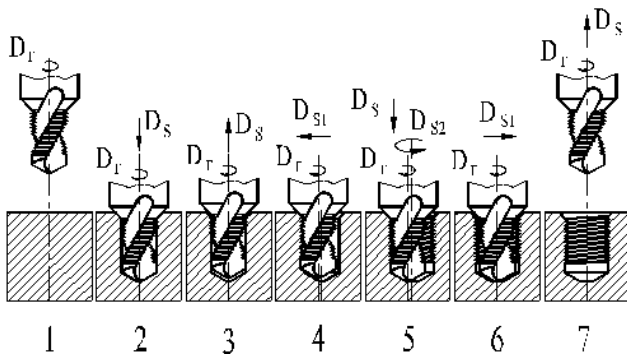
Типовая технологическая последовательность обработки ОСП сверло-резьбофрезой
